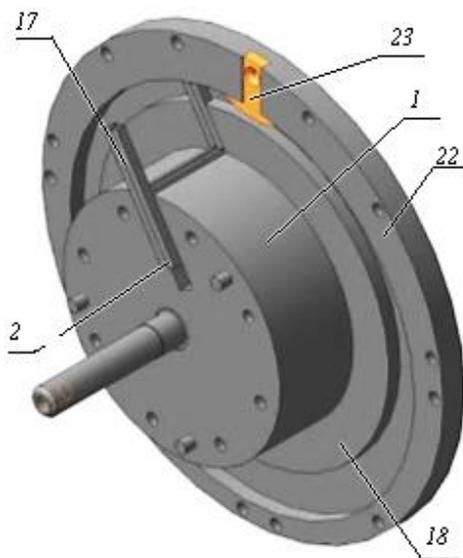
Механизм «утапливания» рабочей заслонки: 1 – ротор компрессора; 2 – заслонка ротора компрессора; 17 – выступ рабочей заслонки; 18 – боковые щеки ротора компрессора; 22 – щека корпуса двигателя; 23 – утапливатель
